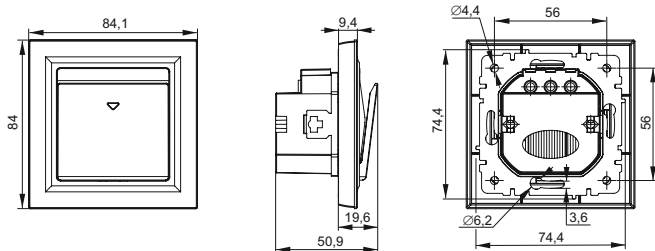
Габаритные размеры выключателя / Figure 2 – Overall dimensions of switch /
